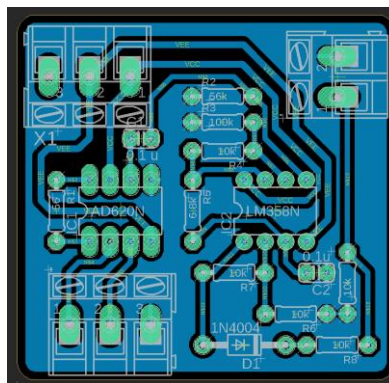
Diseño de la PCB del Sensor EMGs hecha en EAGLE®.
